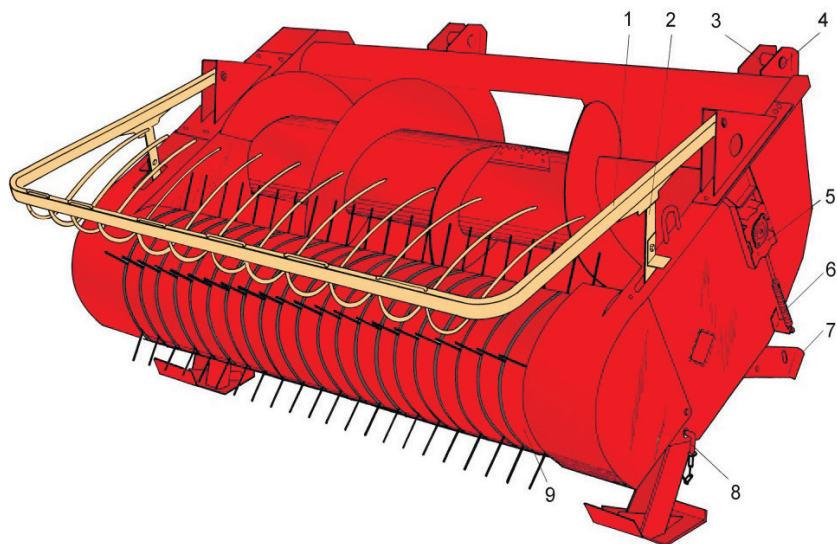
Подборщик: 1 – прижимное приспособление; 2 – стойка; 3 – верхний ловитель; 4 – ось; 5 – опоры шнека; 6 – пружины; 7 – нижний ловитель; 8 – фиксатор; 9 – подбирающий барабан; 10 – шнек; 11 – башмак
